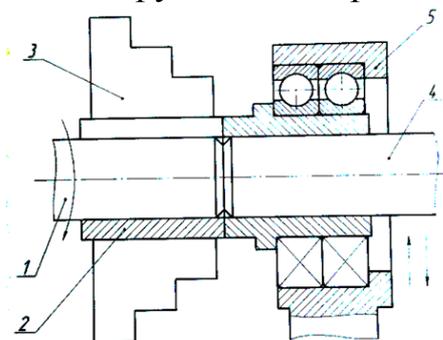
Схема разделения прутка на заготовки винтовой прокаткой
